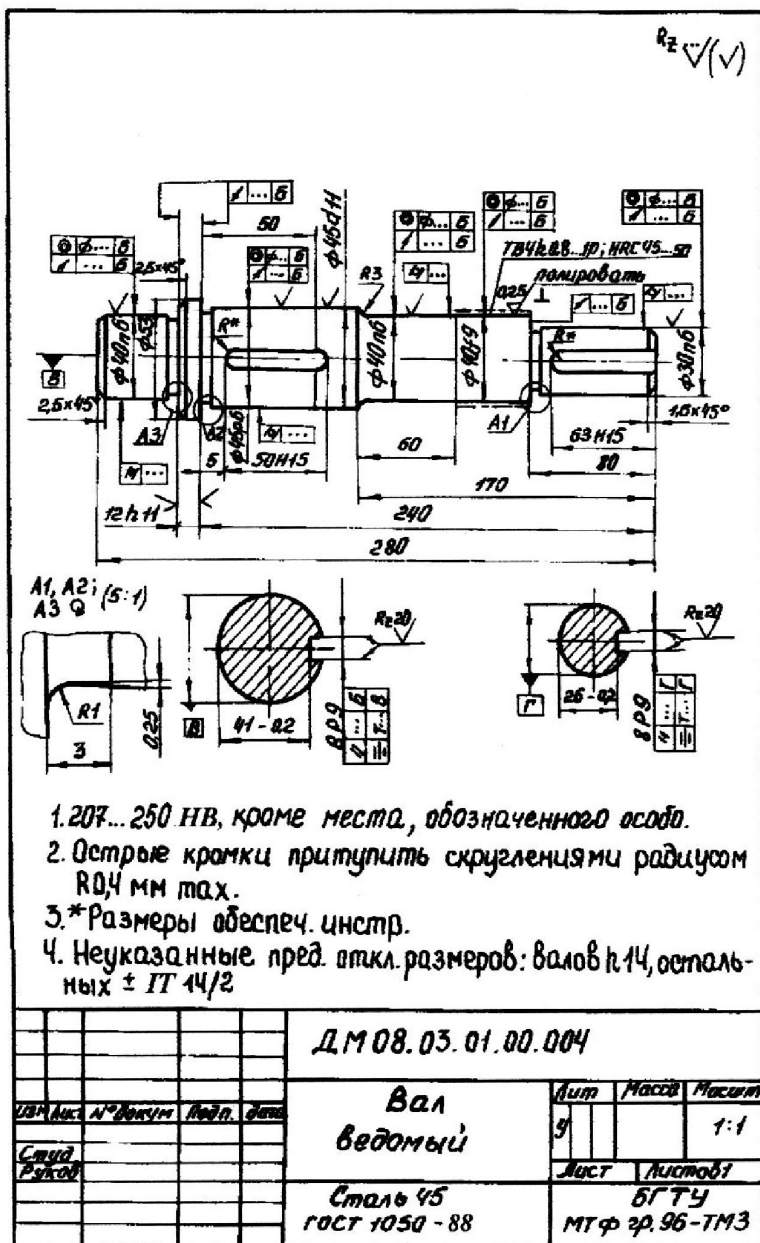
Пример выполнения рабочего чертежа вала редуктора
